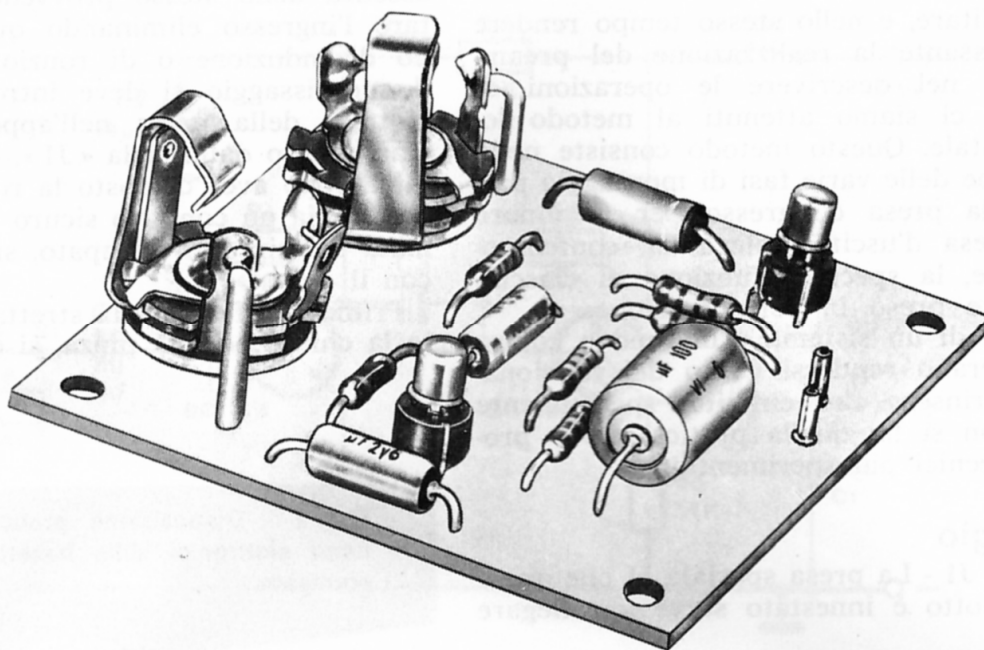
Disegno illustrativo della basetta a circuito stampato a montaggio ultimato.
